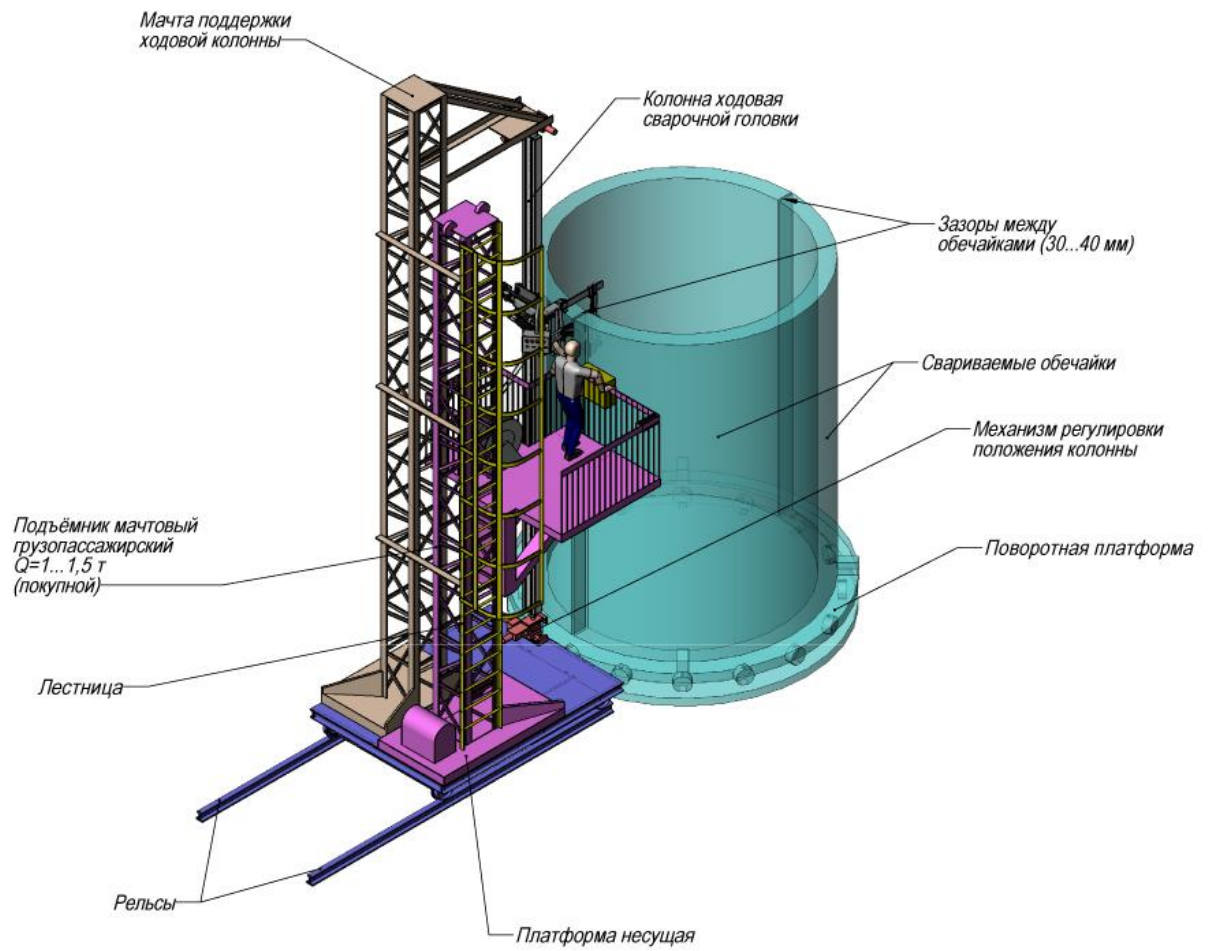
«Сварка обечайек установкой на платформе»[21]
